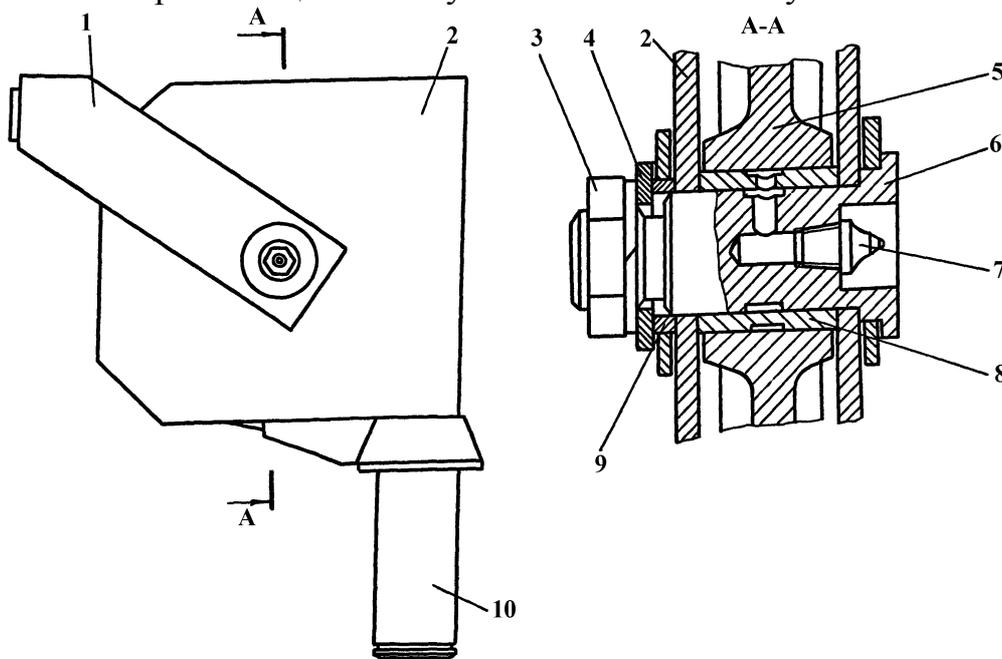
Верхний канатонаправляющий блок: 1 – направляющая; 2 – корпус; 3 – гайка; 4, 9 – шайбы; 5 – ролик; 6, 10 – оси; 7 – масленка;
